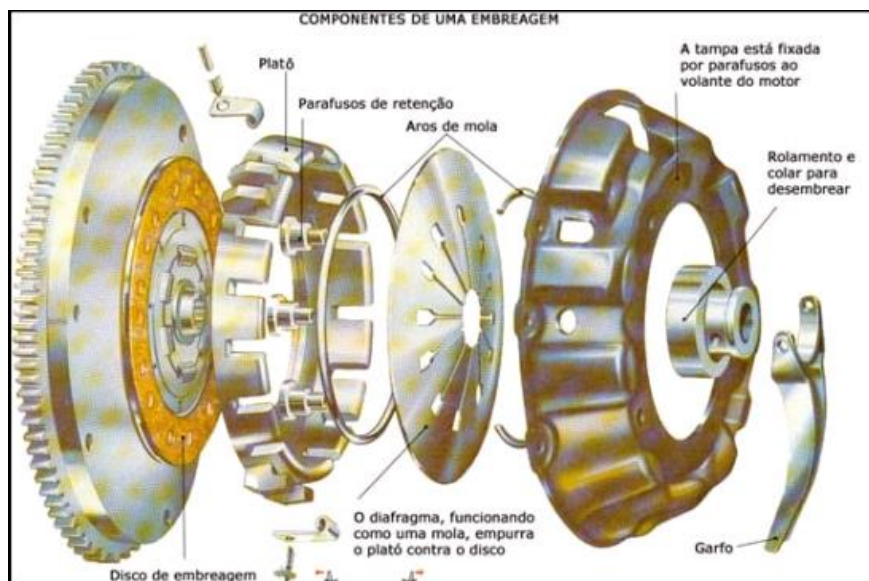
Principais componentes de um conjunto de embreagem automotiva [23]
